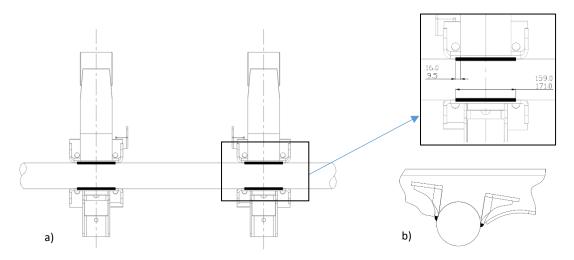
Soldadura brazo a eje. a) Vista inferior, b) Vista lateral (Acot.: mm)
